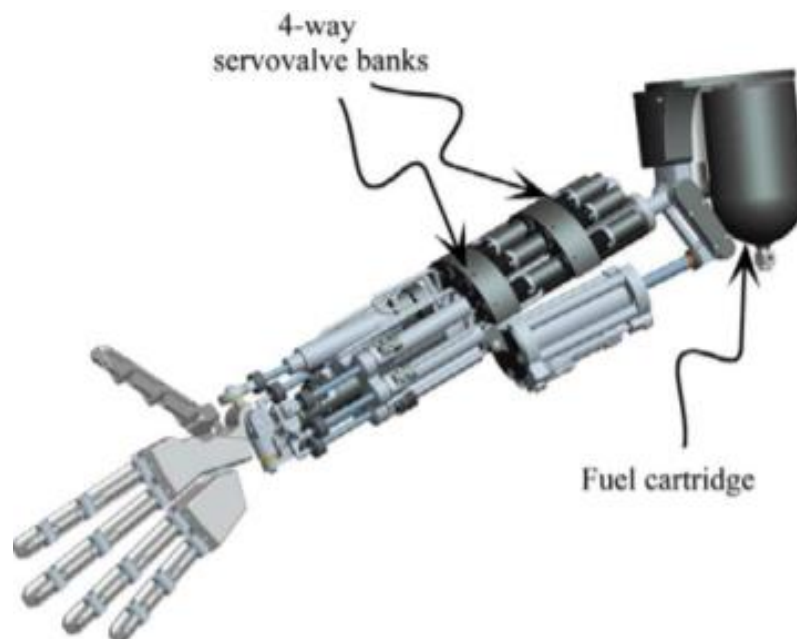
Brazo neumático desarrollado por la Universidad de Vanderbilt [10]
